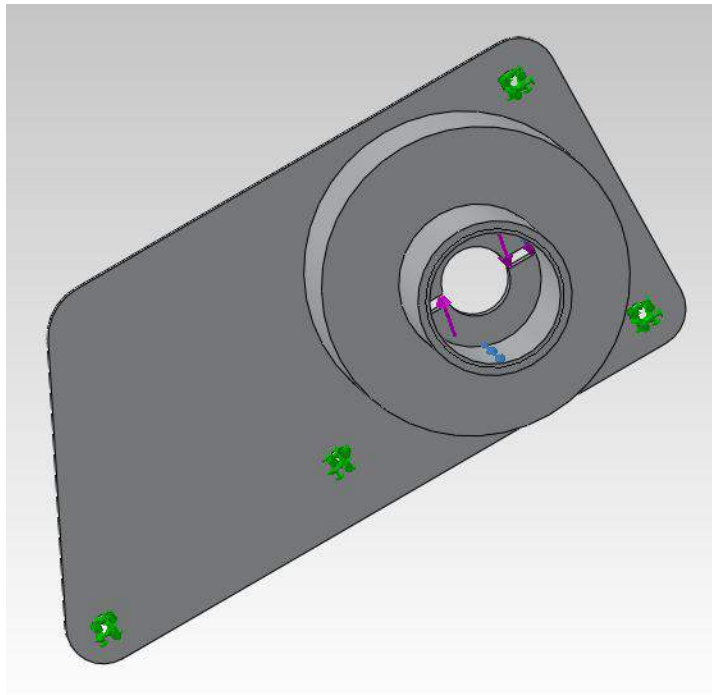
Caja engranajes externa con cargas y restricciones.
